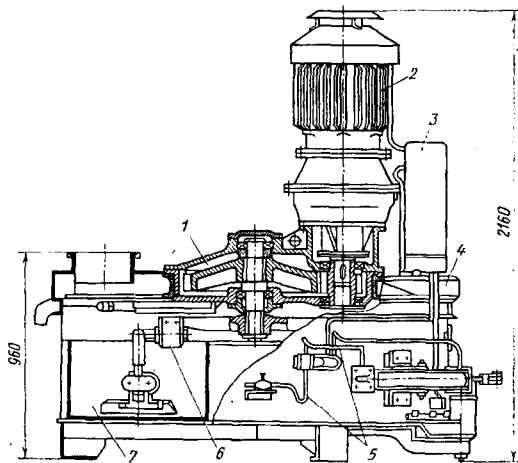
Роторный бетономеситель: 1 – крышка корпуса редуктора; 2 – мотор-редуктор; 3 – электрооборудование; 4 – рама; 5 – пневмопривод затвора; 6 – смешивающий аппарат; 7 – корпус (чаша).
